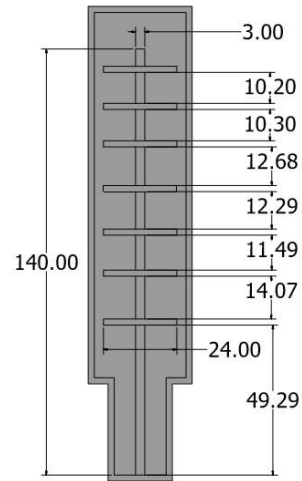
Dimensiones del molde superior. Vista superior. Medidas dadas en milímetros (mm)
